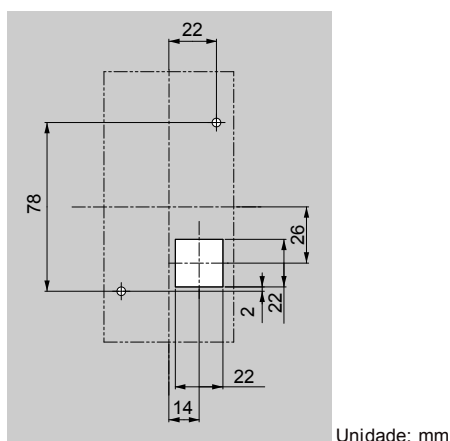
Dimensões de recorte do painel (instalação de montagem na superfície/externa)
